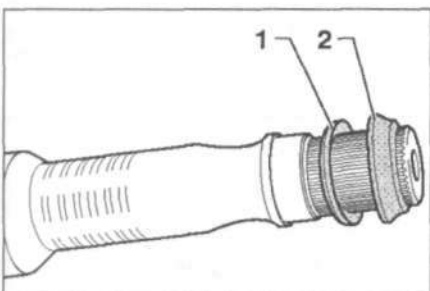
Установочное положение тарельчатой шайбы и упорной шайбы на наружном шарнире:
